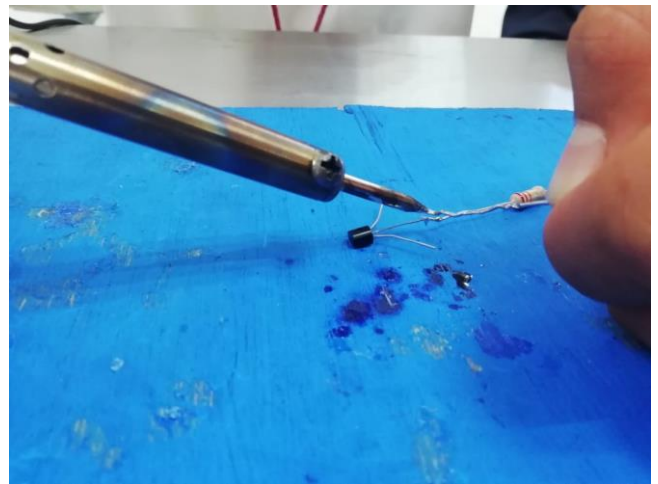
Soldar la base del transistor con una punta de la resistencia.
